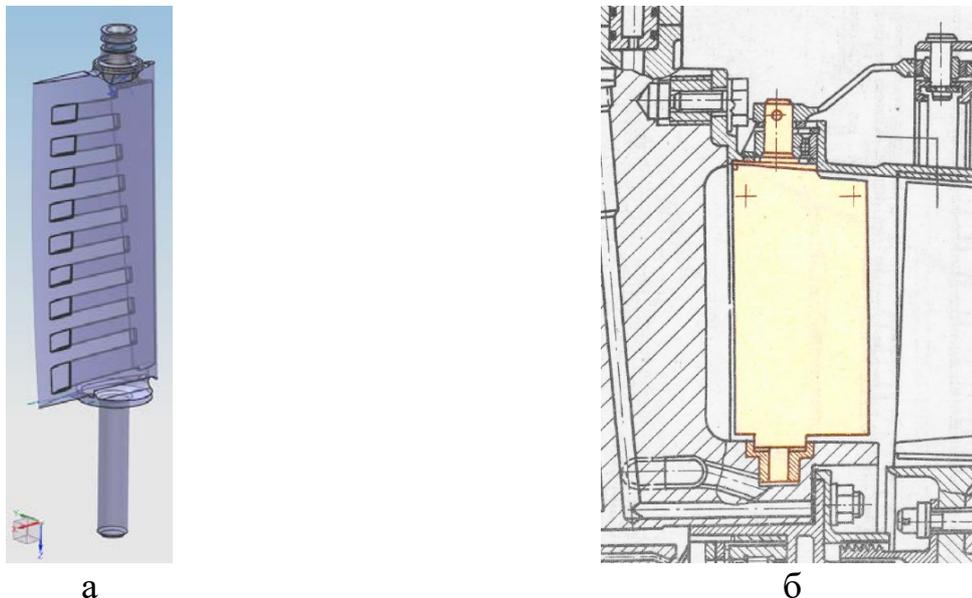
Обогреваемая лопатка ВНА с ПОС: а – 3Д-модель лопатки, б – расположение лопатки в корпусе первой опоры двигателя
